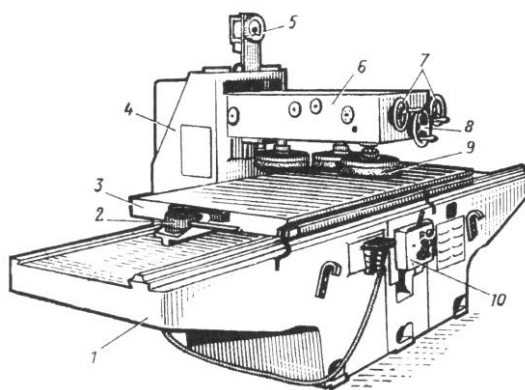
Глянсувальний верстат ГЛП: 1 - станина; 2 - механізм кріплення деталей; 3 - каретка; 4 - тумба; 5 - амперметр; 6 - супорт; 7 - механізм піднімання дисків; 8 - механізм піднімання супорта; 9 - ротаційні диски; 10 - панель керування гідроприводом
